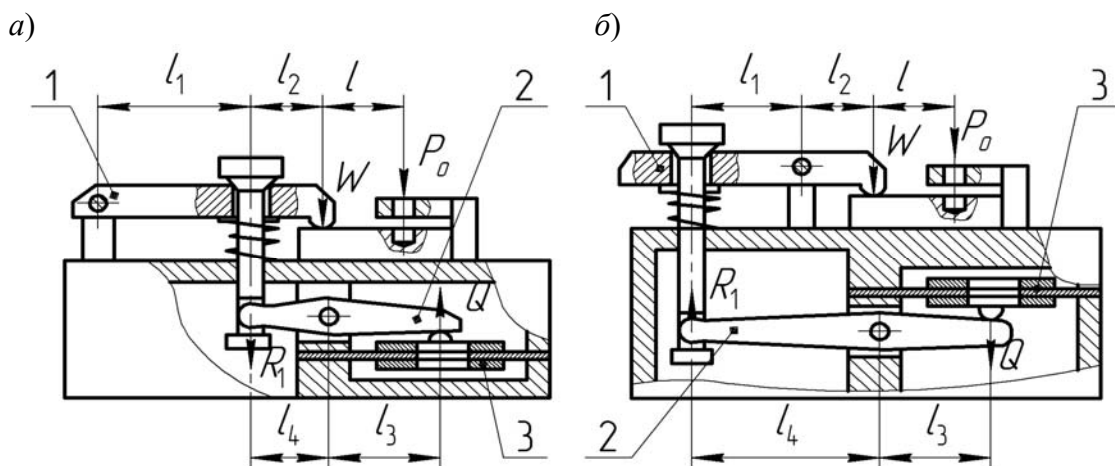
Схемы проектируемых станочных приспособлений
